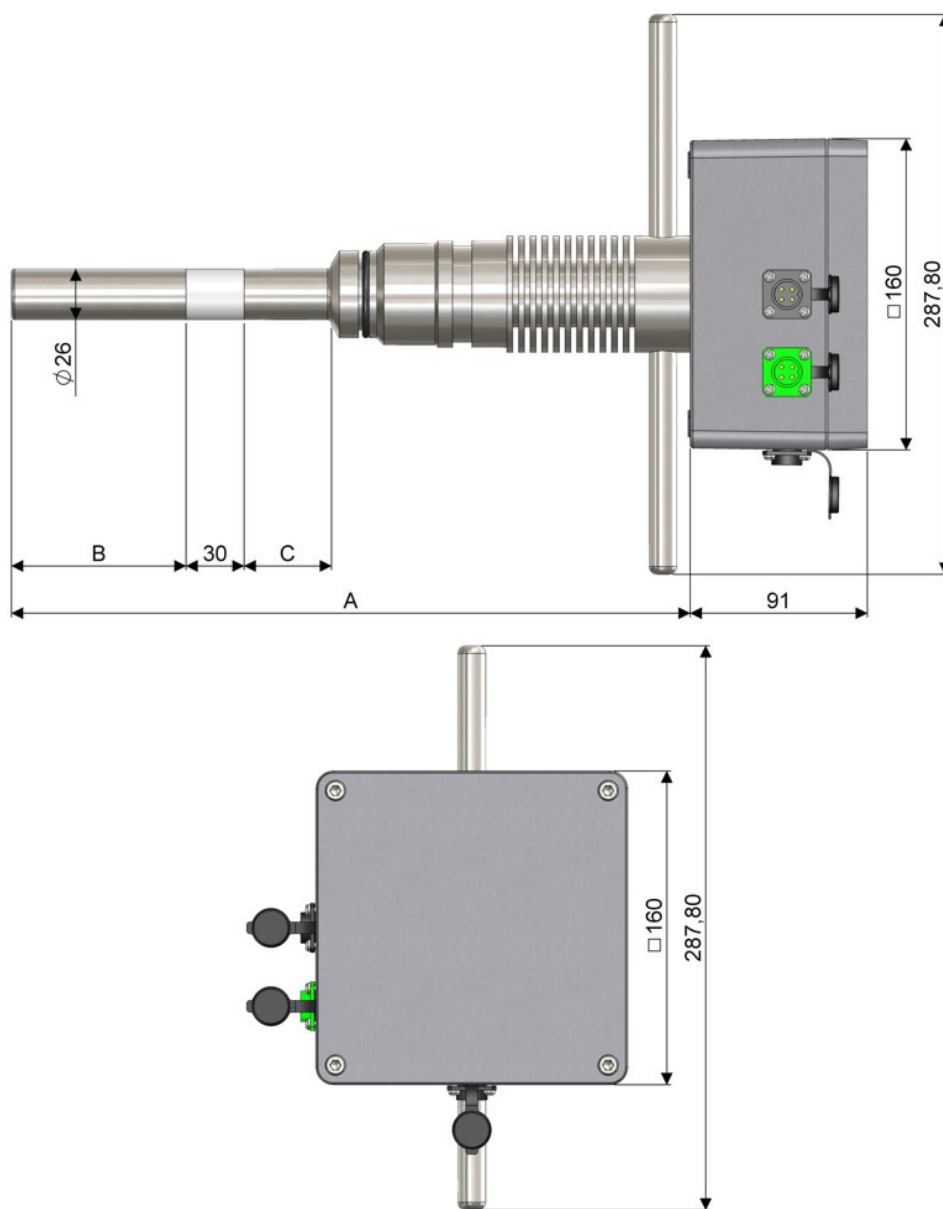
Dimensionamento para montagem do Transmissor (Cotas em milímetro)
